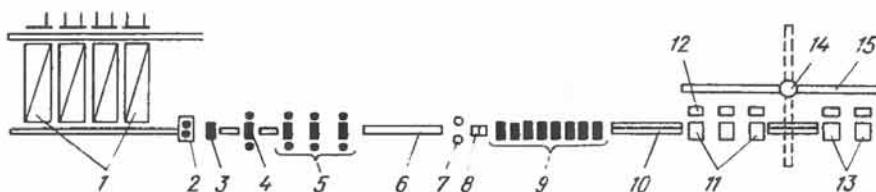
Схема расположения оборудования непрерывного широкополосного стана 2000:
